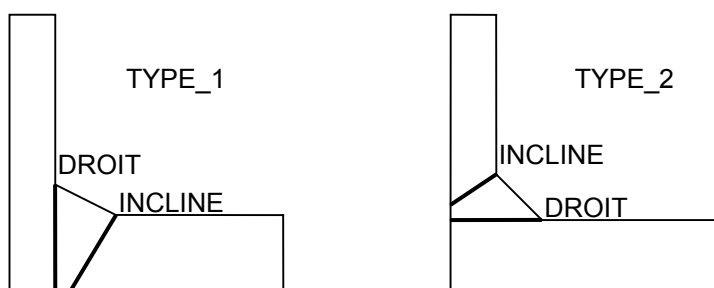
a : Définition de la position d'une fissure suivant le type de la soudure
